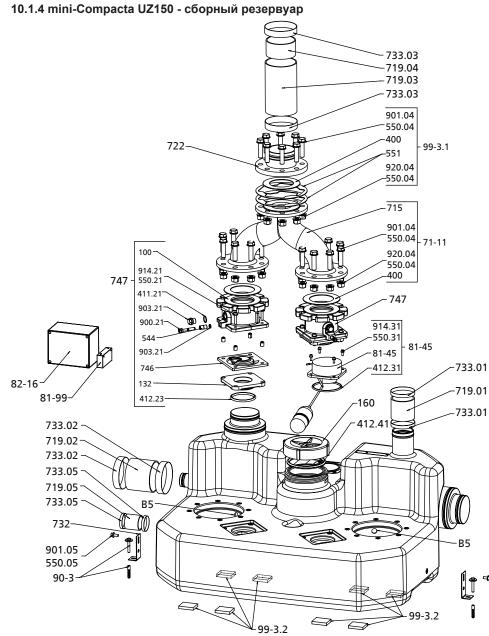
Деталировочный чертеж mini-Compacta UZ150 - сборный резервуар
